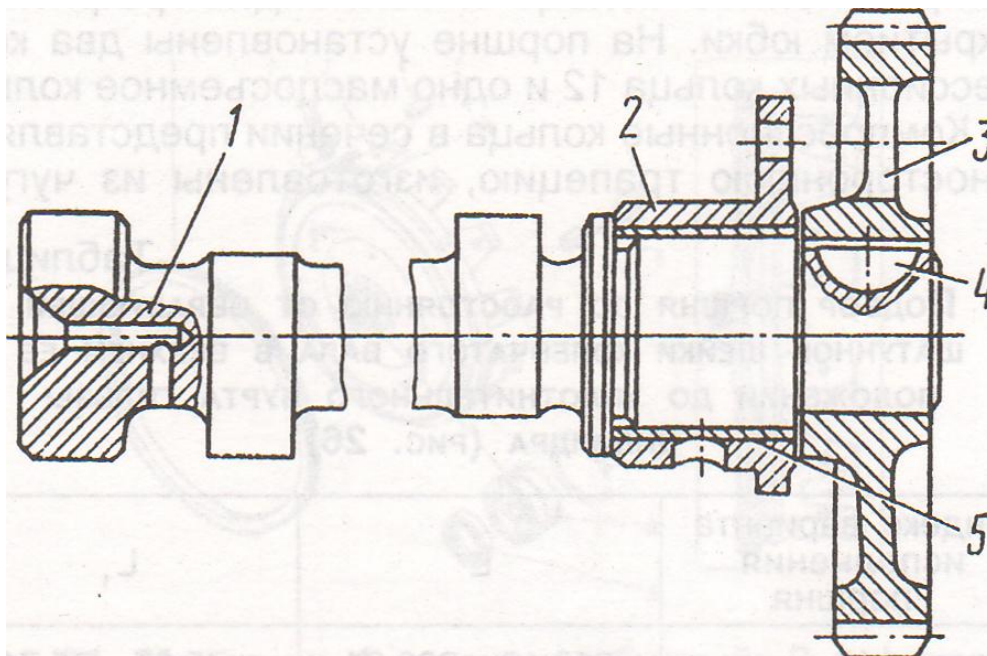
Распределительный вал в сборе: 1 - вал распределительный; 2 - корпус заднего подшипника; 3 - шестерня; 4 - шпонка; 5 – подшипник
